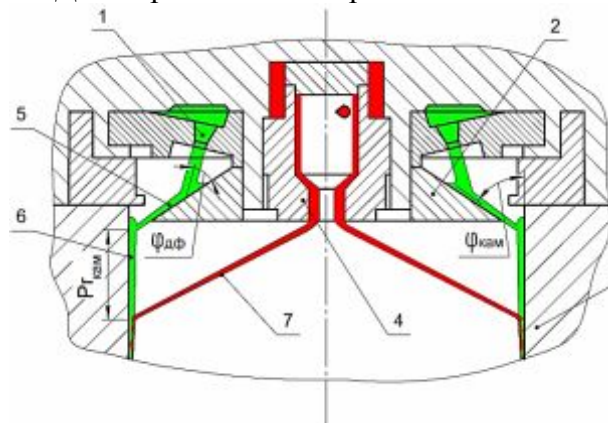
Дефлекторно-центробежный смесительный элемент форсуночной головки: 1-струйная форсунка окислителя; 2-дефлектор; 3-стенка камеры сгорания; 4-центробежная форсунка горючего; 5-первичная плёнка окислителя; 6-вторичная плёнка окислителя; 7-факел распыла центробежной форсунки
